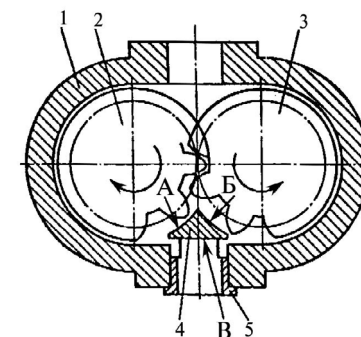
Схема шестеренного гідромотора з пристроєм для покращення пуску: 1 – корпус; 2 і 3 – шестірни зовнішнього зачеплення; 4 - пристрій для покращення пуску; 5 – втулка.
